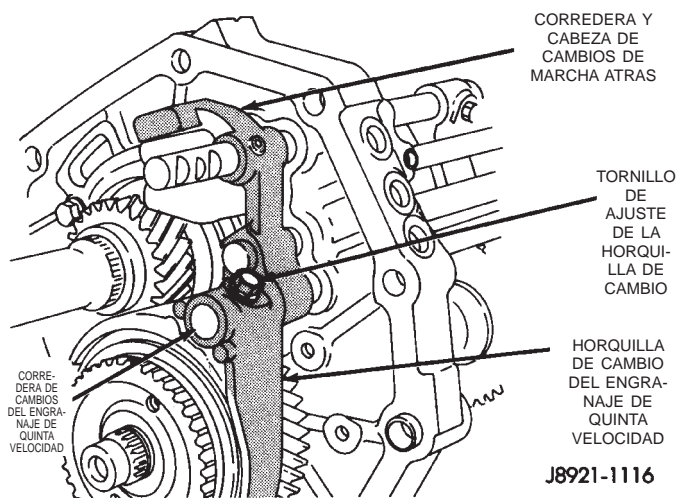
Instalación del perno de retención de la horquilla de cambio del engranaje de quinta velocidad
